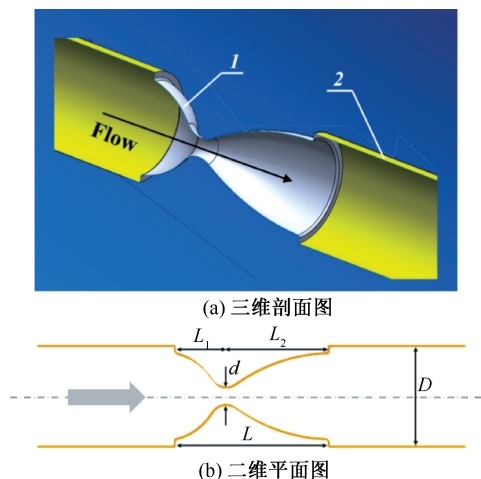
第 2 代激波雾化喷嘴的三维剖面图和二维平面图
